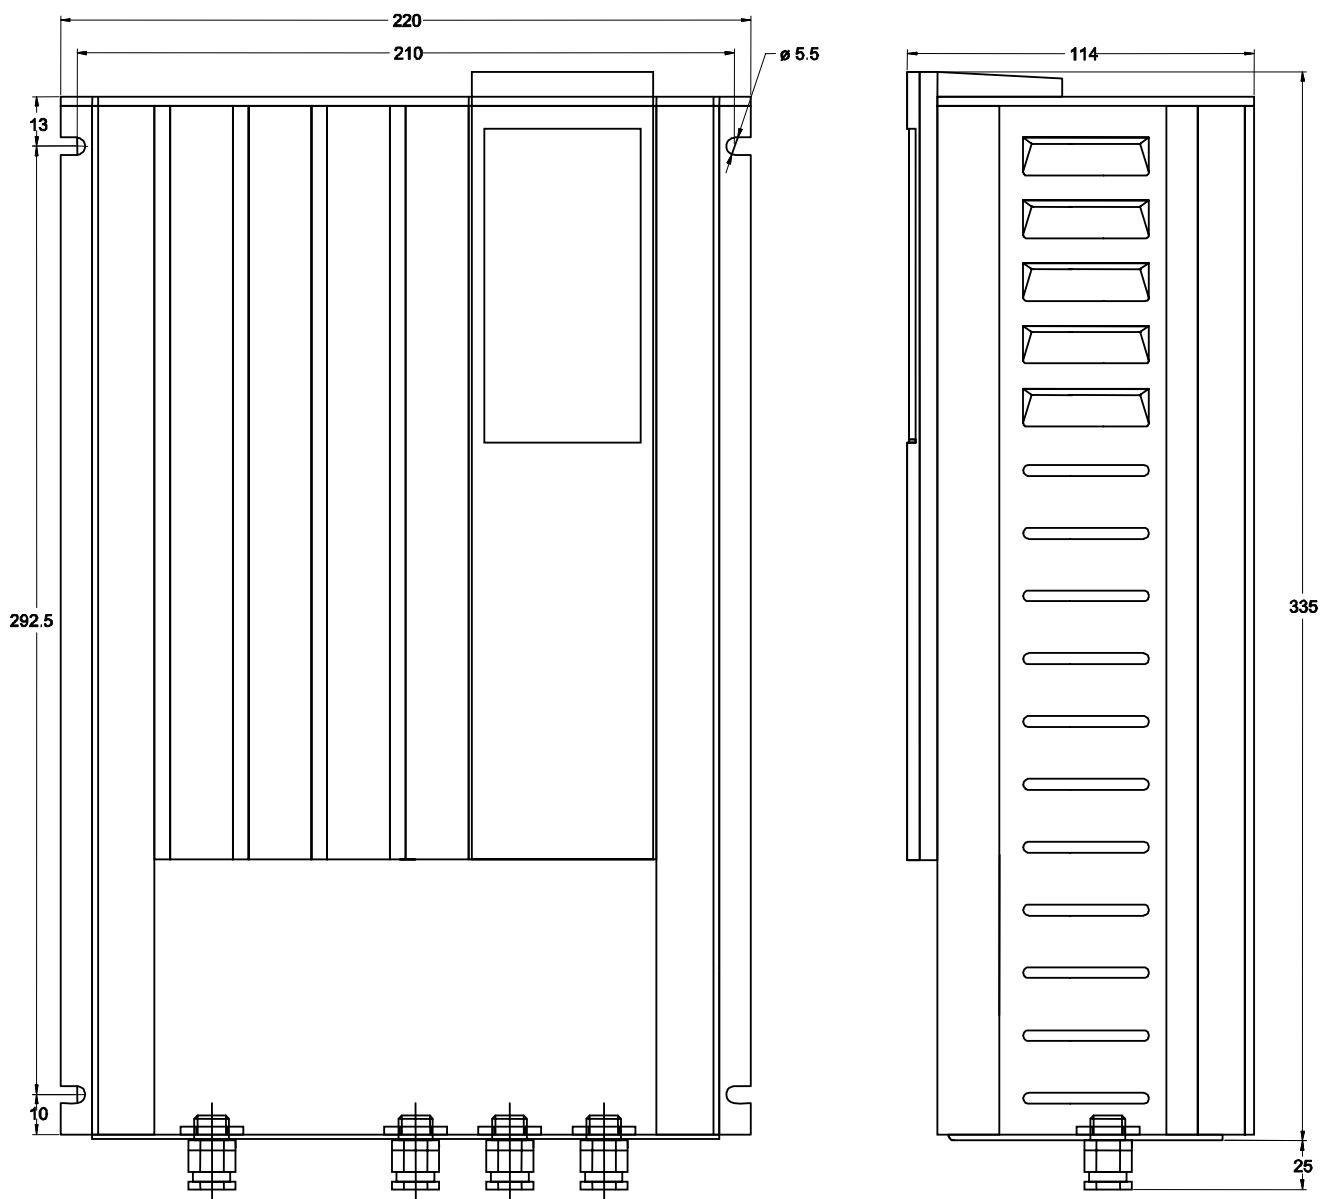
Abmessungen des Wechselrichters Mass Sine 12/800, 24/800 & 48/500
